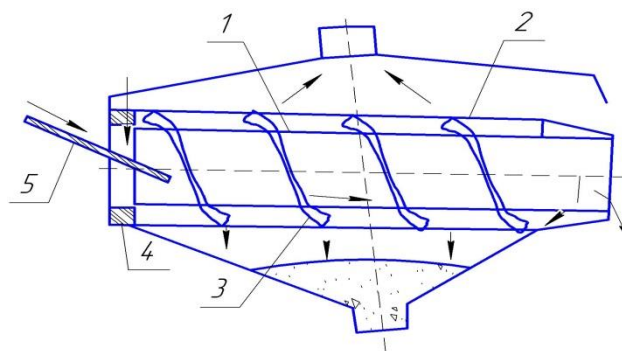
Галтовочный барабан непрерывного действия для очистки
